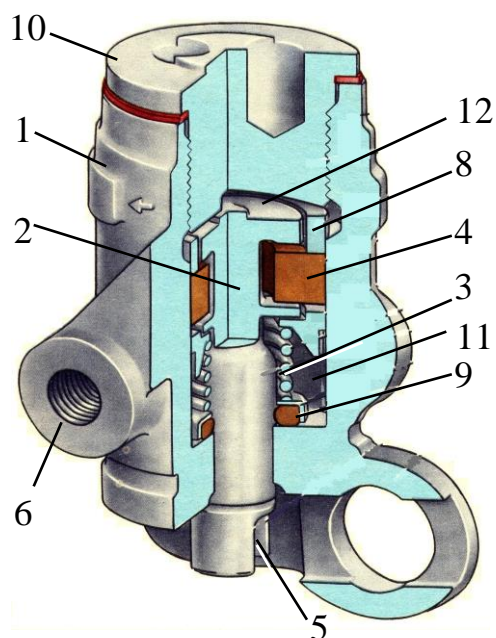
Конструкция регулятора тормозных сил при разделении тормозного привода отдельно на передние и отдельно на задние колеса: 1 – корпус; 2 – поршень; 3 – пружина; 4 – седло клапана; 5 – вырез для П-образного рычага; 6 – вход от главного тормозного цилиндра; 8 – распорная втулка; 9 – уплотнительное кольцо; 10 – пробка; 11 – полость нормального давления; 12 – полость регулируемого давления
